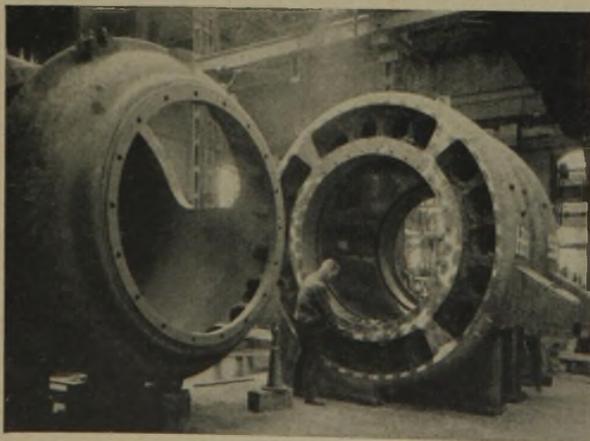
N.D.-Zylinder und Zwischenstück für Großgaskompressor
